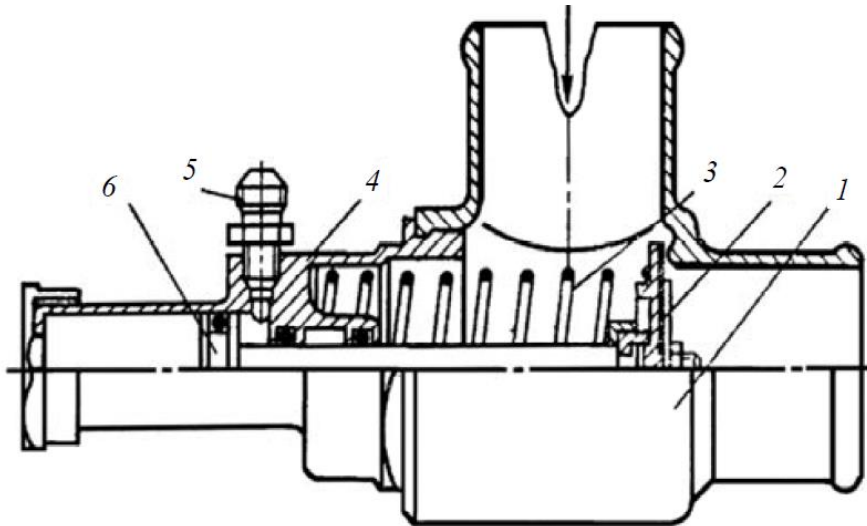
Схема крану аварійного зливу палива в польоті: 1 – корпус; 2 – клапан; 3 – зворотна пружина; 4 – втулка; 5 – штуцер; 6 – поршень
